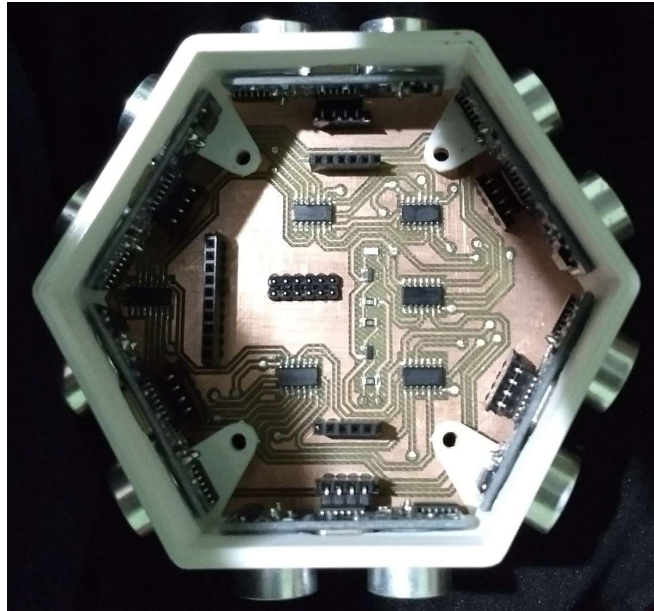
Parte inferior del PCB de sensores ultrasónicos.
